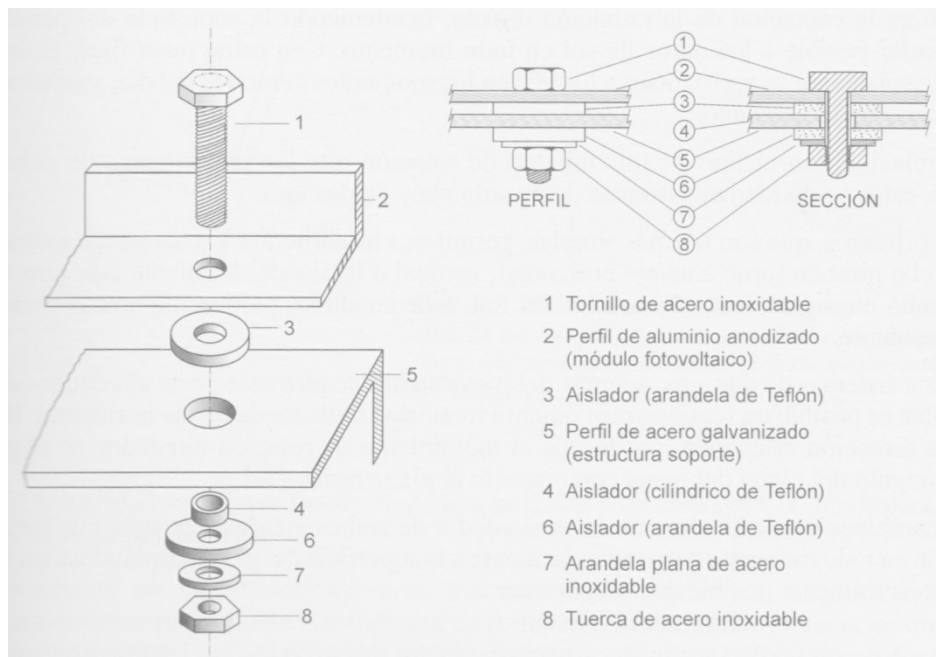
Detalle de la fijación del panel a la estructura con las correspondientes arandelas aislantes (fuente: CENSOLAR)
